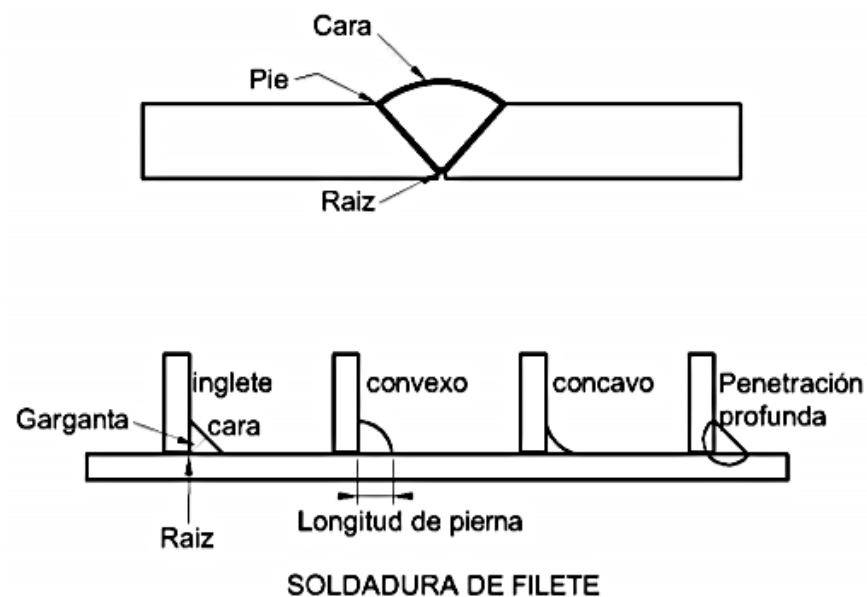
Terminología usada en el diseño y fabricación de uniones soldadas
